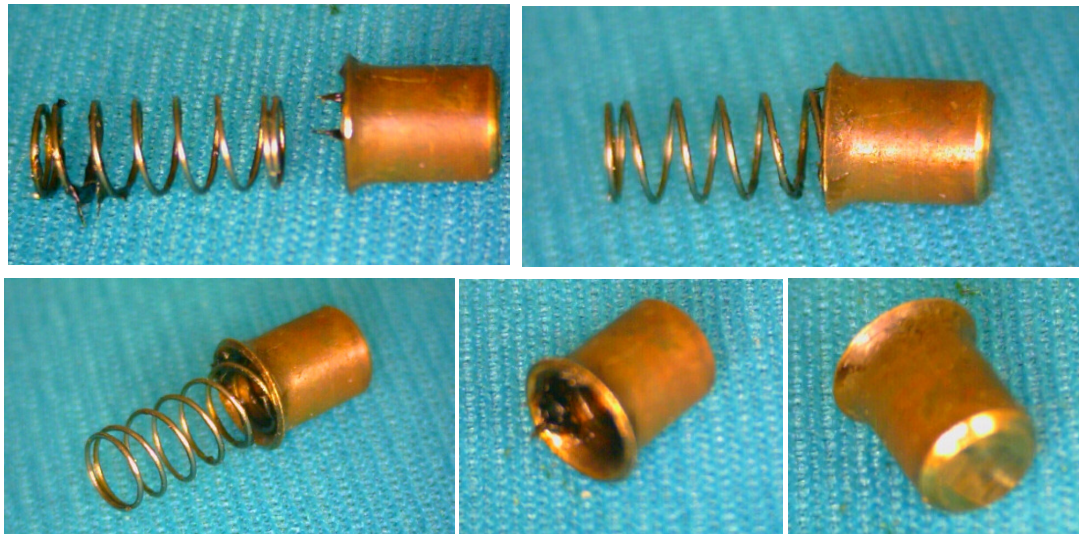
Kontaktzylinder mit Schraubendruckfeder
